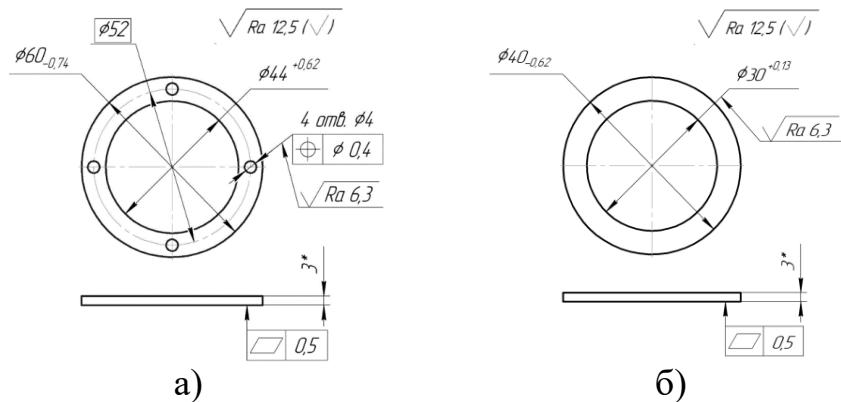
Чертежи кольцевых деталей: а - «Фланец»; б - «Кольцо упорное»
